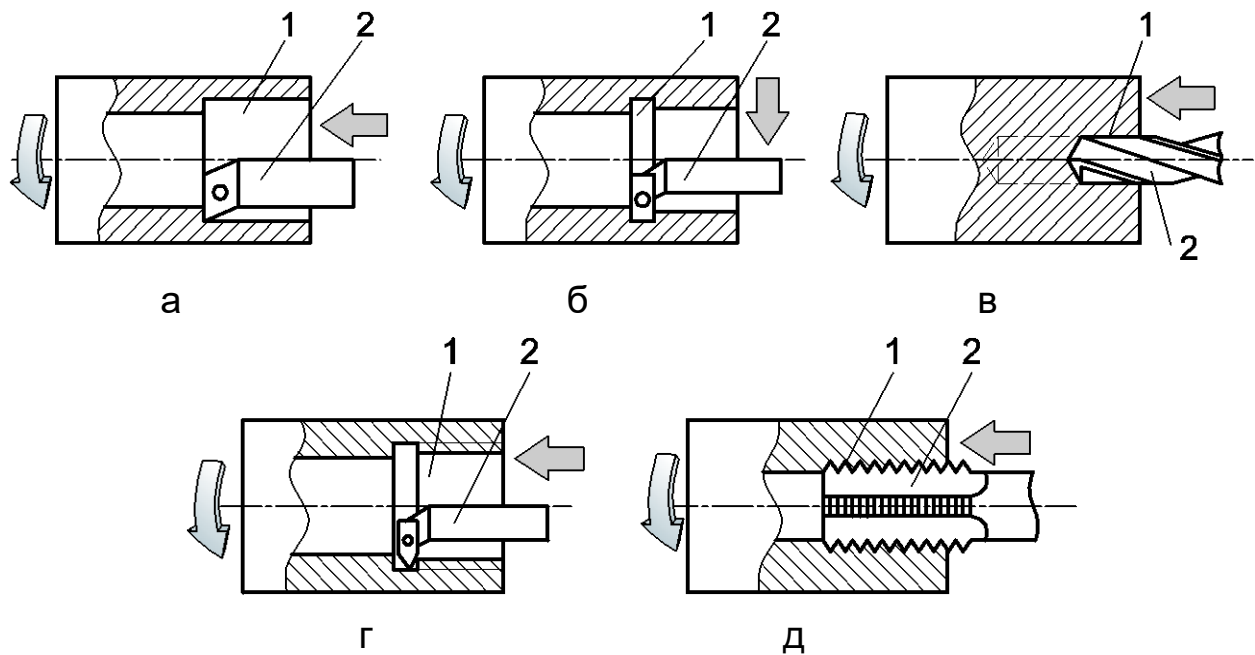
Способы токарной обработки внутренних поверхностей
